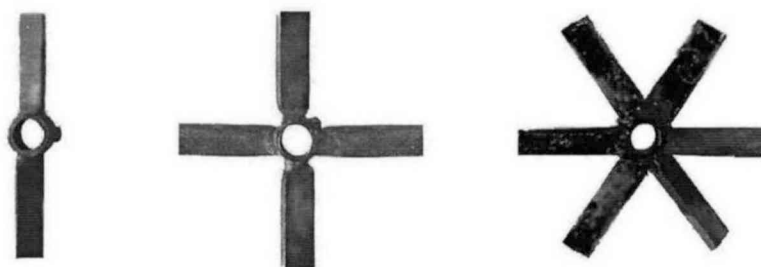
Конструкція робочих органів лабораторної дробарки трапецієвидною формою лопатей та кутом нахилу профілю 90°
